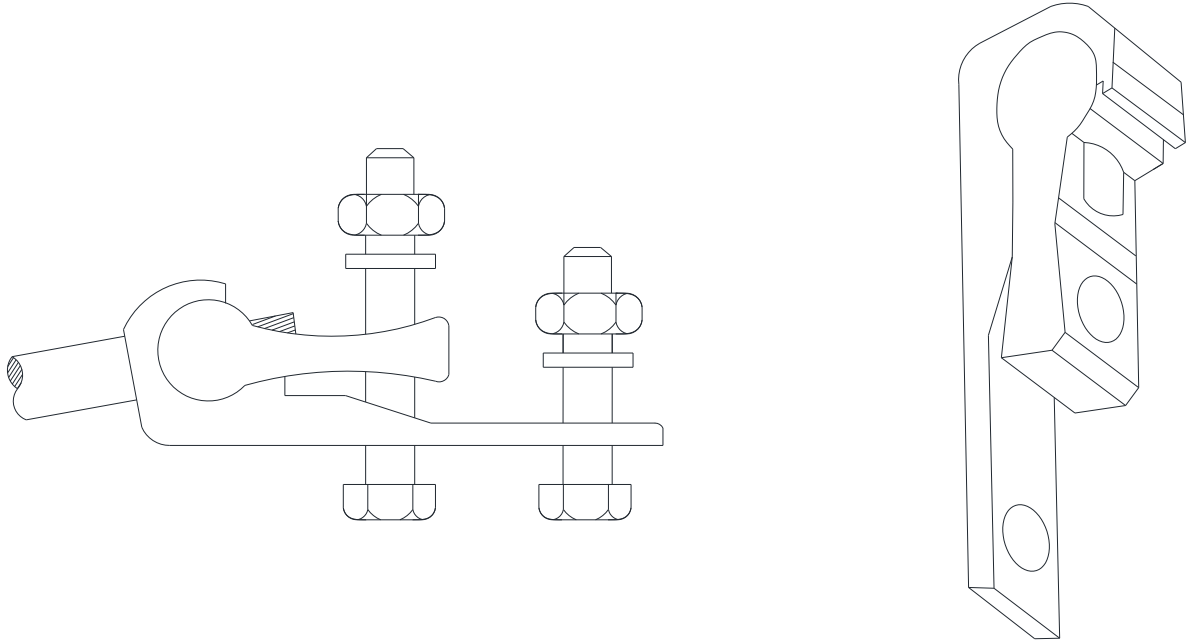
Conexões e emendas – Conector de compressão tipo “C” com estribo
